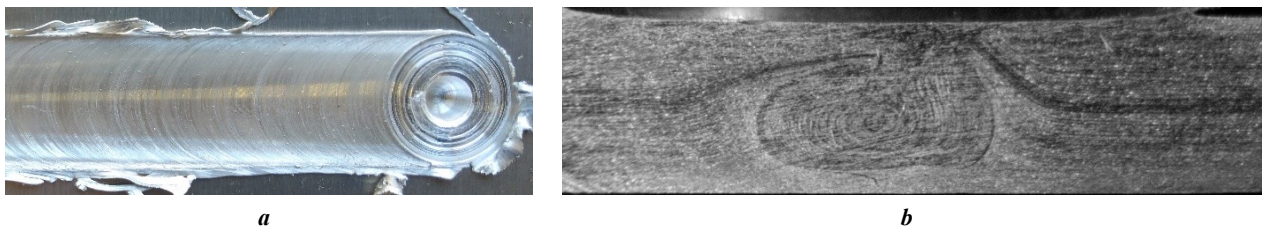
Внешний вид (a) и макрошлиф (b) поперечного сечения сварного соединения, полученного инструментом с конической формой пина (рис. 1 б).
